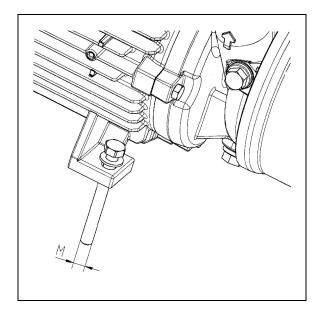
Elementi di fissaggio per avvitare i piedi al pavimento
